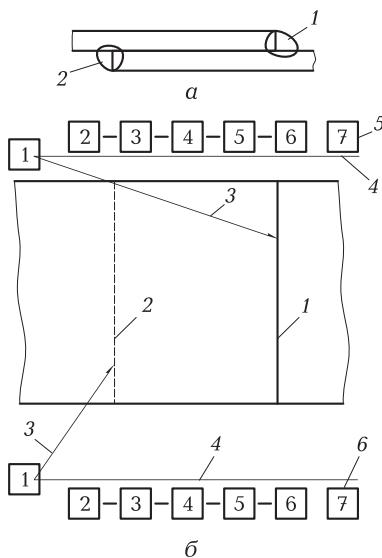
Обозначения сварных швов на чертежах:
